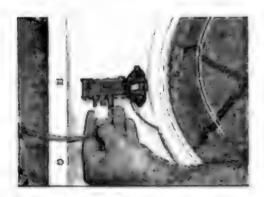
Отсоединение проводое от устройства блокировки люка
